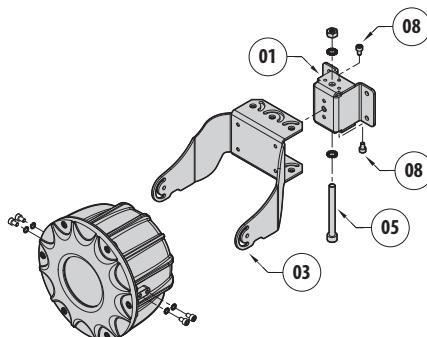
Fixação em parede com entrada de cabos por baixo.
